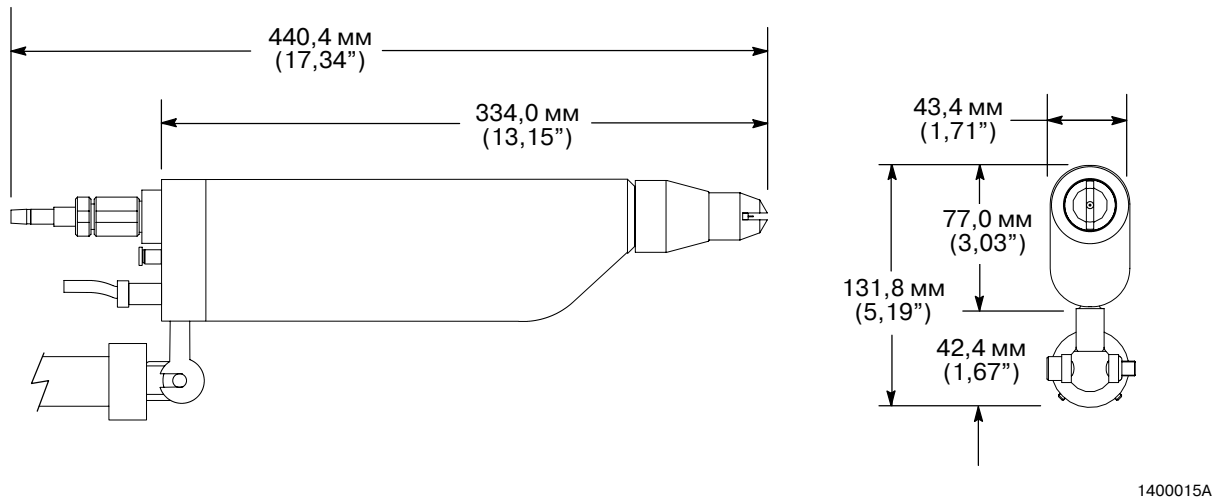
Размеры автоматического штангового порошкового распылителя Sure Coat
